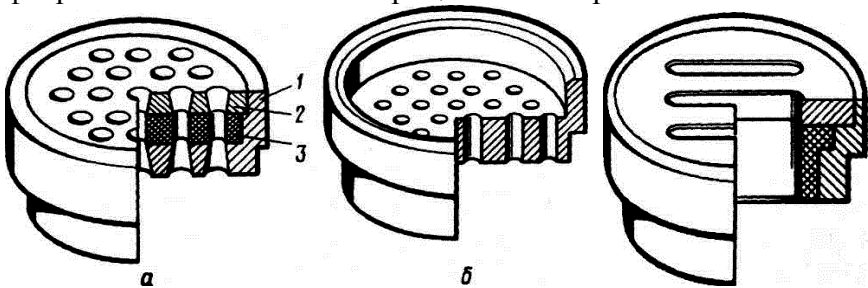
Дискові вставки макаронних матриць: а, б - з формуючими отворами для вермішелі; 1 - корпус; 2 - диск; 3 - прокладка фторопластова; в - з формуючими отворами для локшини
